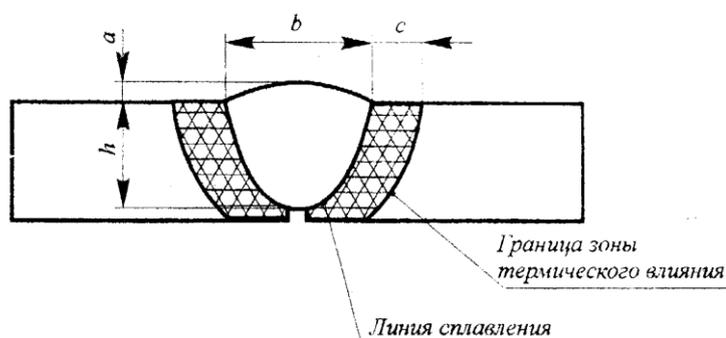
Основные параметры шва и ЗТВ: a – высота усиления; b – ширина шва; c – ширина ЗТВ; h – глубина проплавления
